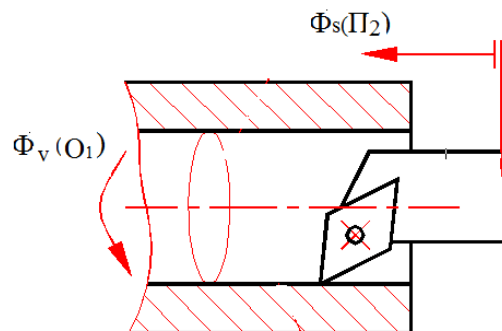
Формоутворюючі рухи при токарному обробленні внутрішньої поверхні
